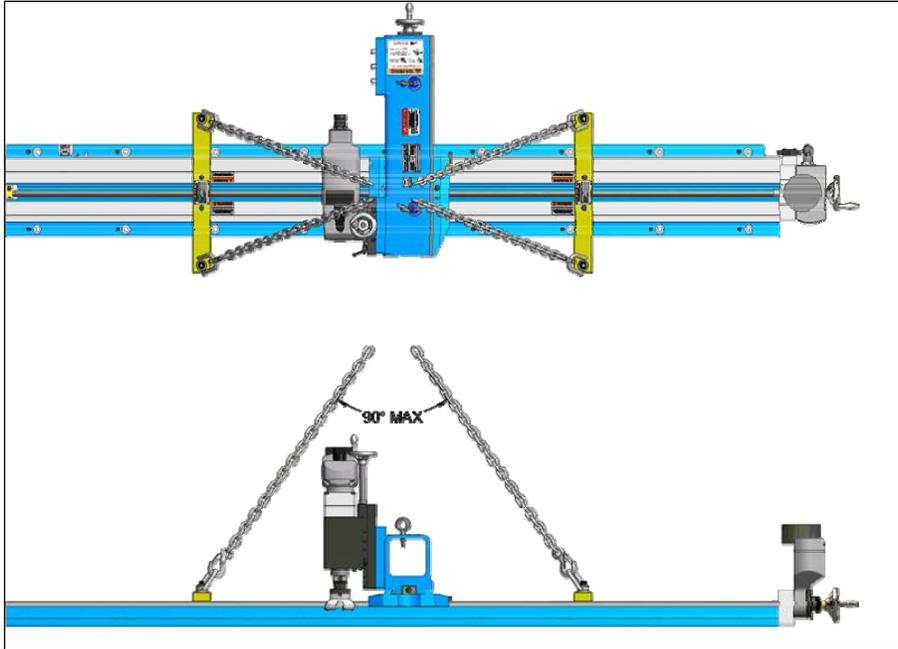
LEVAGE PLAT - HORIZONTAL
